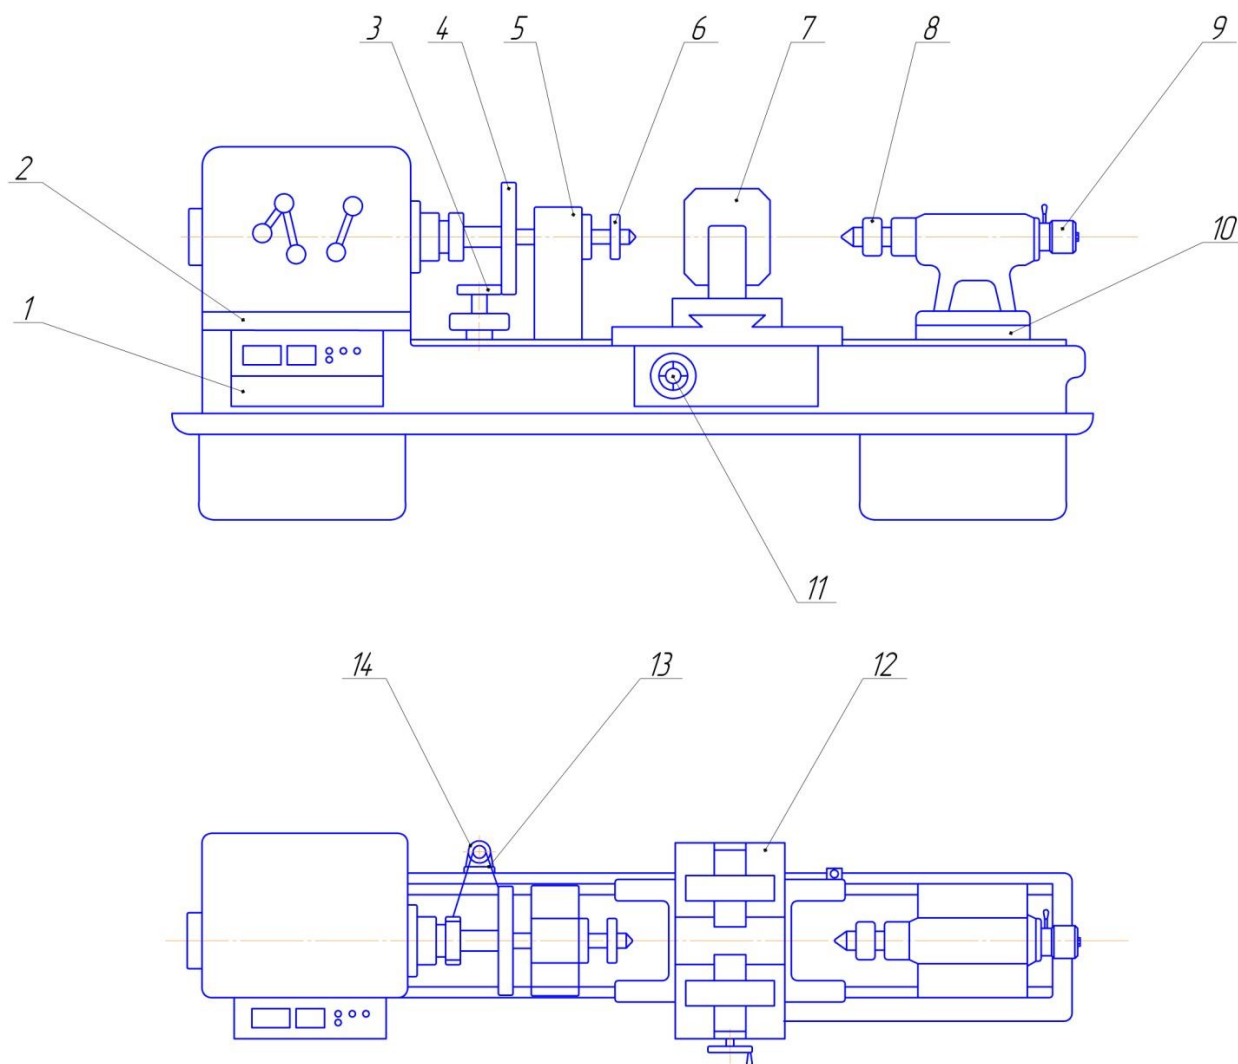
Модернізований токарний верстат для зовнішнього циліндричного магнітно - абразивного полірування
